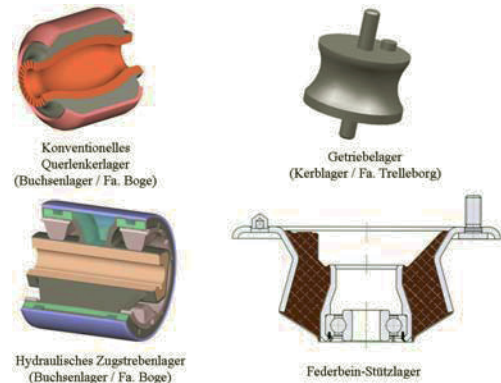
Bauformen von Gummi/Metall-Lagern
